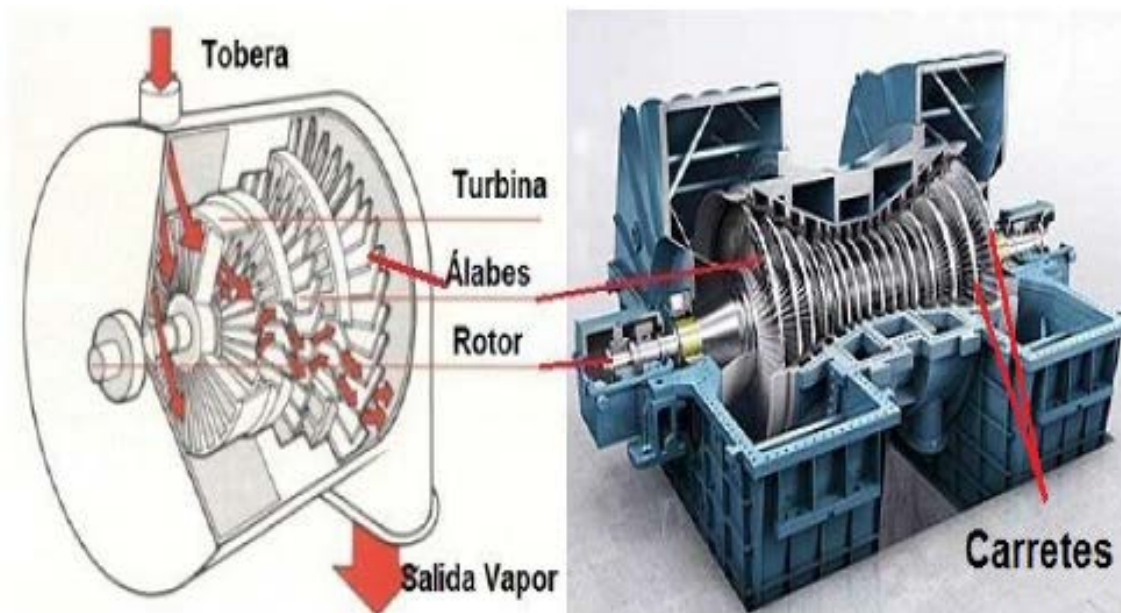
Esquema de una turbina de vapor de alta presión. Fuente: <http://www.areatecnologia.com/mecanismos/turbina-de-vapor.html> (2016).
